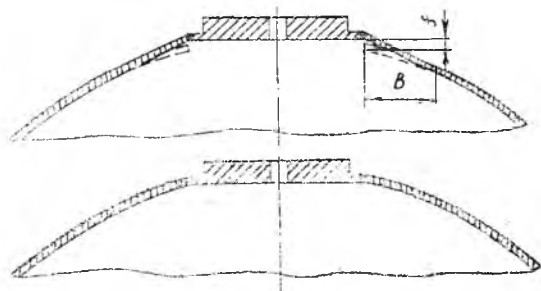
Зона кругового отверстия на оболочке после выштамповки и после сварки
